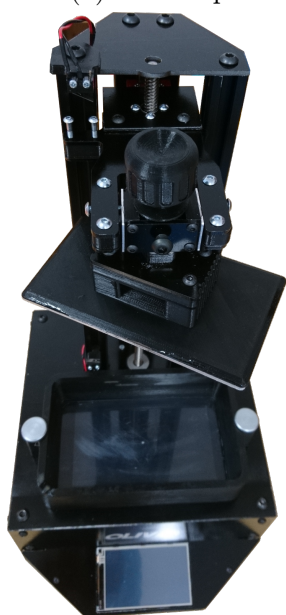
Technická dokumentace ke kalibračnímu mechanismu
